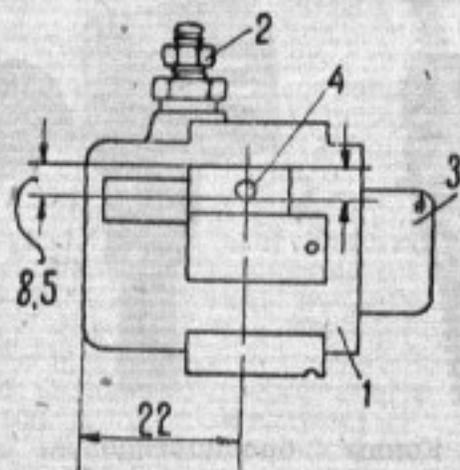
Разметка для сверления отверстия в корпусе замка: 1 — корпус замка; 2 — клемма неподвижной пластинки выключателя для соединения с бобиной; 3 — выступающая часть замка; 4 — отверстие, которое необходимо просверлить диаметром, равным 2—2,5 мм
